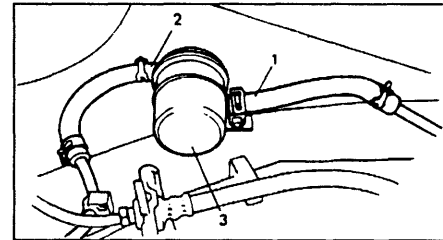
Присоединительные патрубки топливного фильтра. 1 и 2 - впускной и выпускной патрубки, 3 - топливный фильтр.
